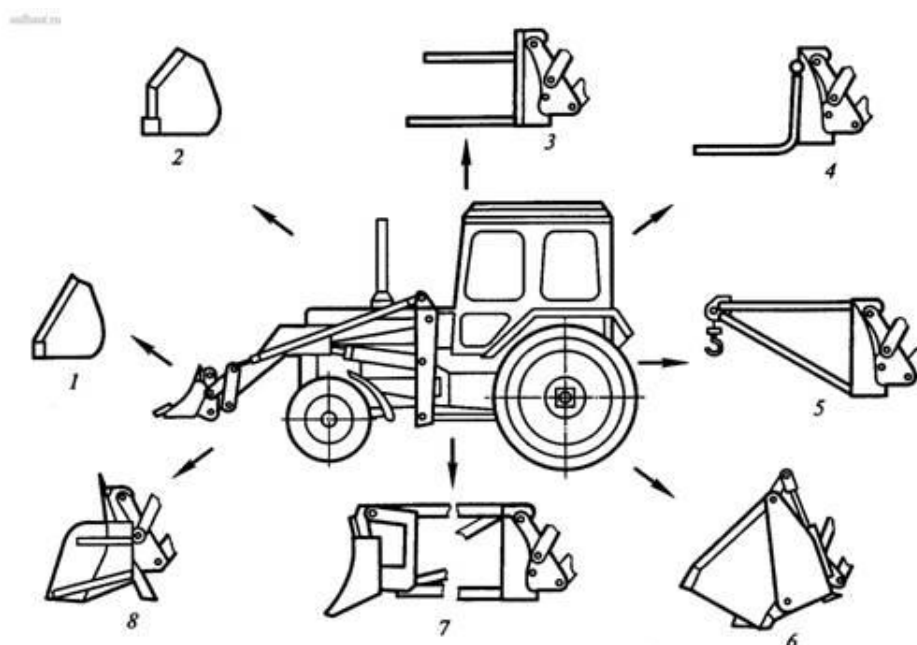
Сменное дополнительное многоцелевое рабочее оборудование бульдозера-погрузчика: 1 - увеличенный ковш; 2 - ковш для снега; 3 - сельскохозяйственные вилы; 4 - грузовые вилы; 5 - монтажный крюк; 6 - челюстной захват; 7 - удлинитель; 8 - уширитель и рыхлитель заднего хода
